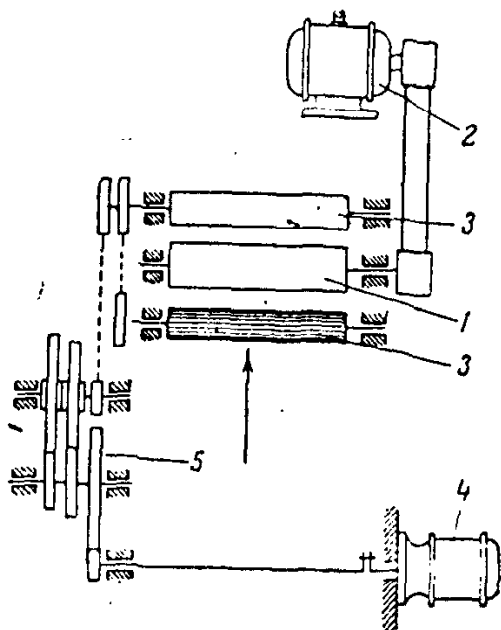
Общий вид одностороннего рейсмусовочного станка типа CP-6-2.
